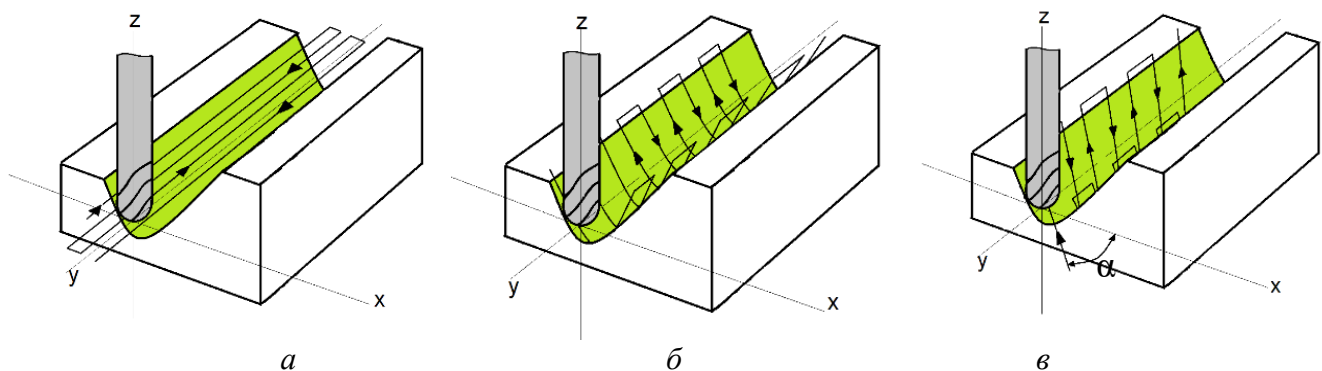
Схема обработки формообразующей поверхности с движением фрезы параллельно к профилю поверхности (а), по нормали к профилю поверхности (б), под углом α (в)
